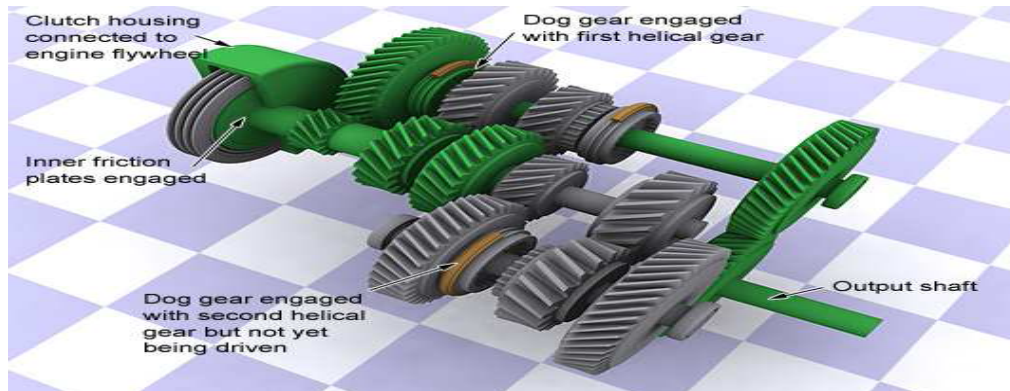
Primera marcha engranada. Segundo engranaje preseleccionado.
